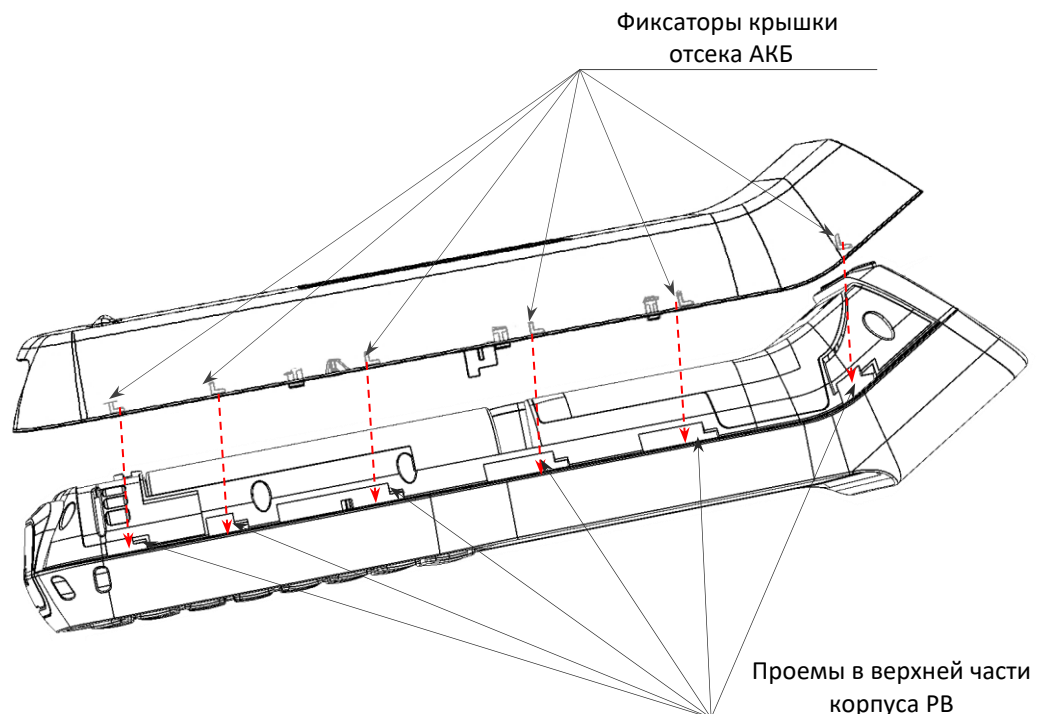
Установка крышки отсека АКБ на верхнюю часть корпуса (расположение фиксаторов и проемов)
